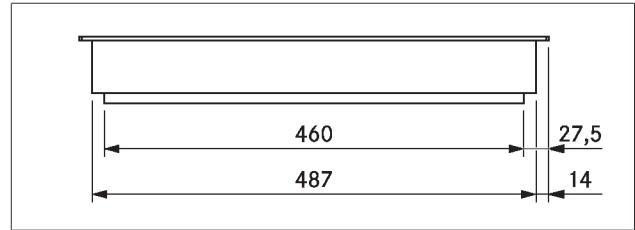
CKT apparatets dimensjoner sett fra siden
